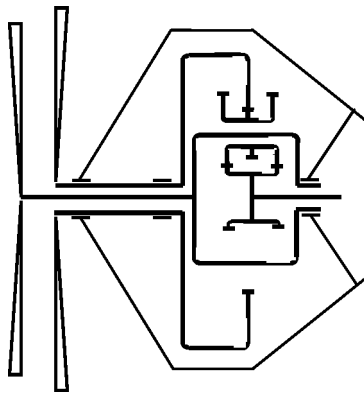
Кинематическая схема редуктора двигателей НК-12
